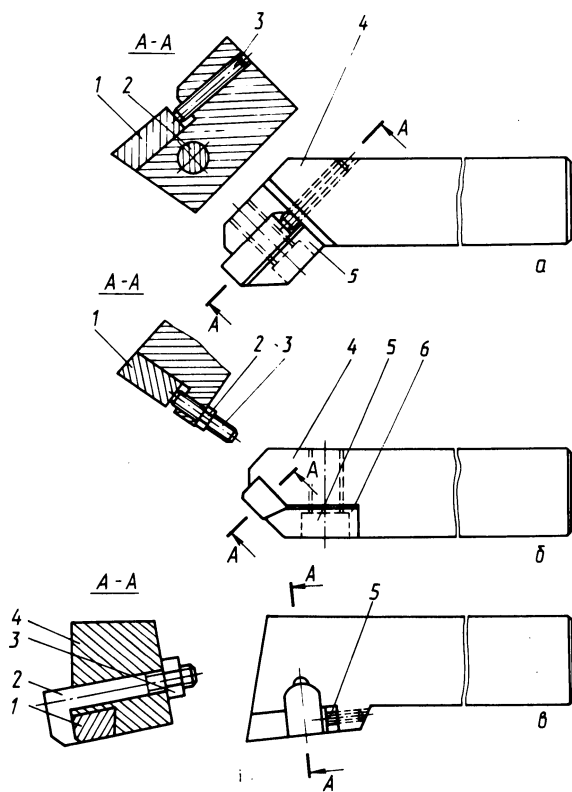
Сборный токарный резец: а – с расположением пластины опорой по большей грани и прихватом сбоку; б – с расположением пластины столбиком и прихватом сбоку; в – с расположением пластины с опорой по боковой стороне и Г-образным прихватом.
